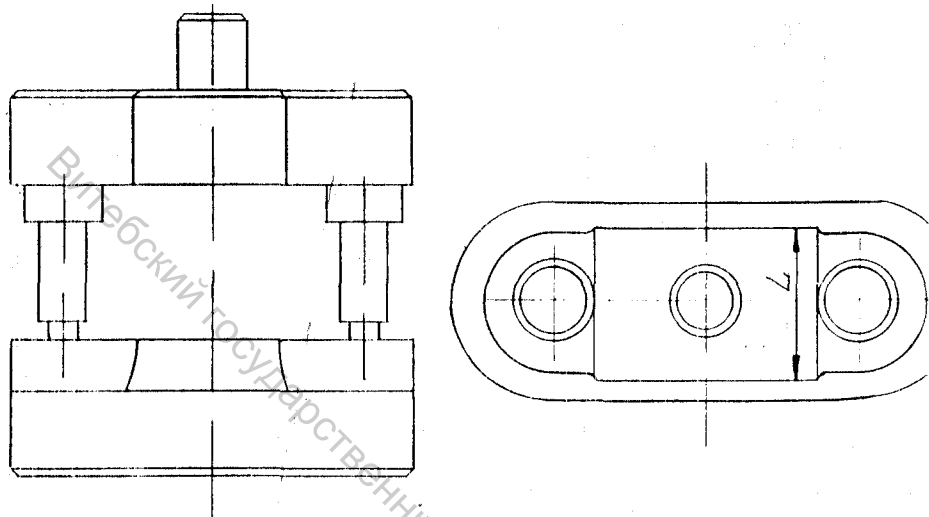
Стандартный блок с осевым (симметричным) расположением направляющих колонок.
